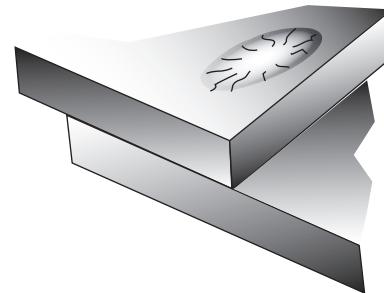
Diseños de junta típicos para la soldadura de arco
